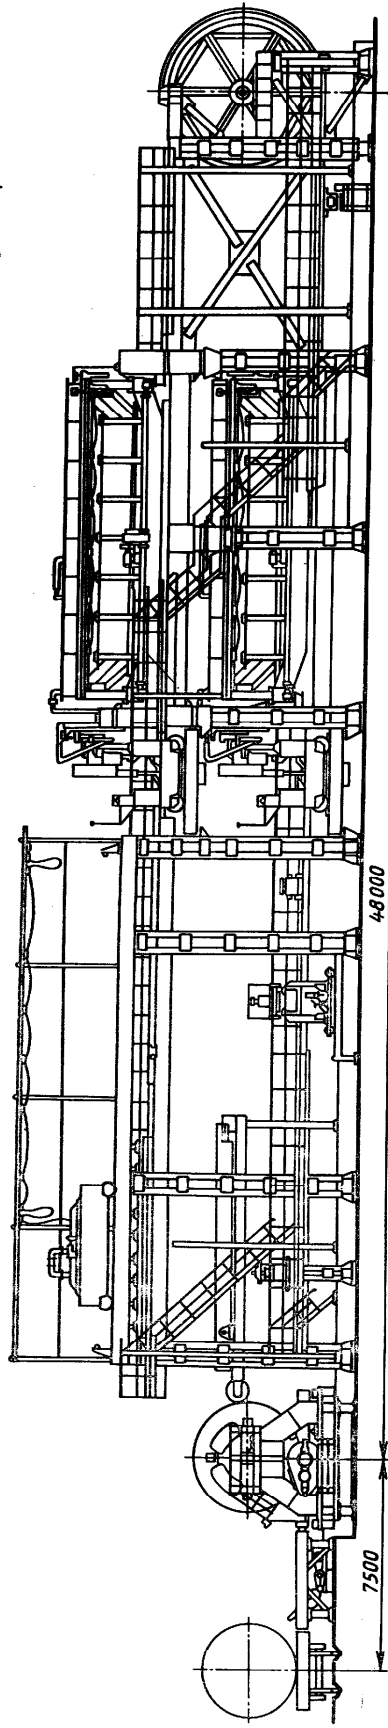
Общий вид установки для изготовления рулонных полотнищ большого размера
